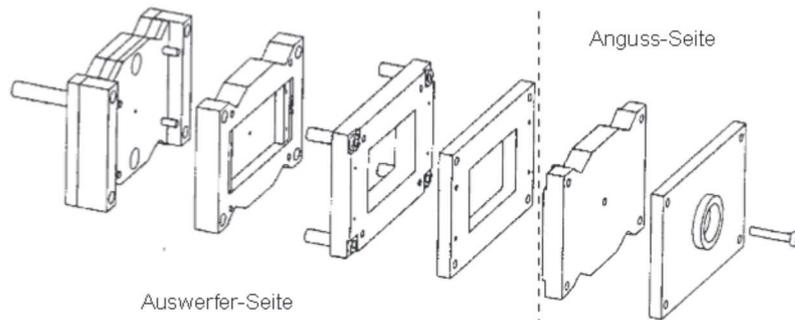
Prinzipieller Aufbau eines Stahlstammwerkzeuges für die Kunststoffspritzgießfertigung, Explosionsdarstellung
